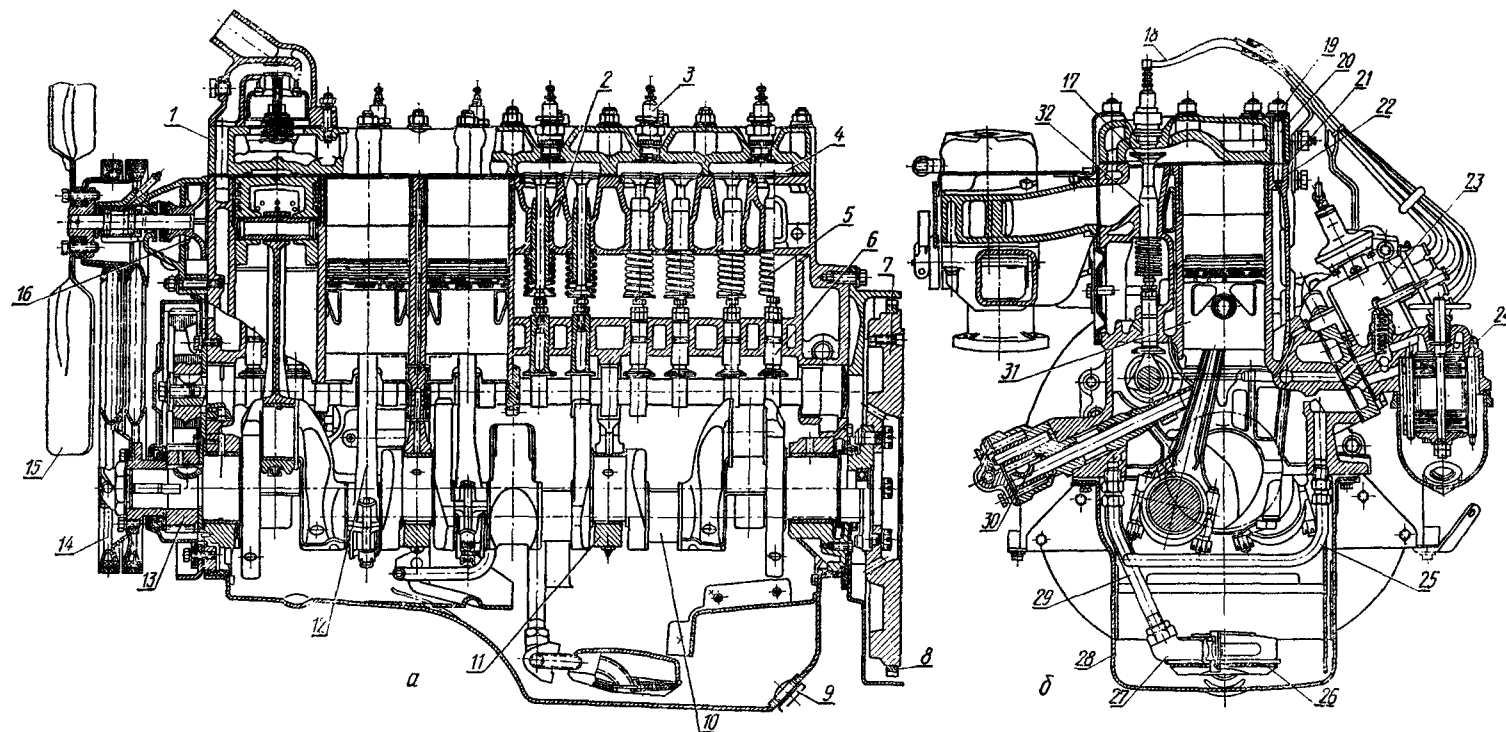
Продольный (а) и поперечный (б) разрезы двигателя ГАЗ-52:
